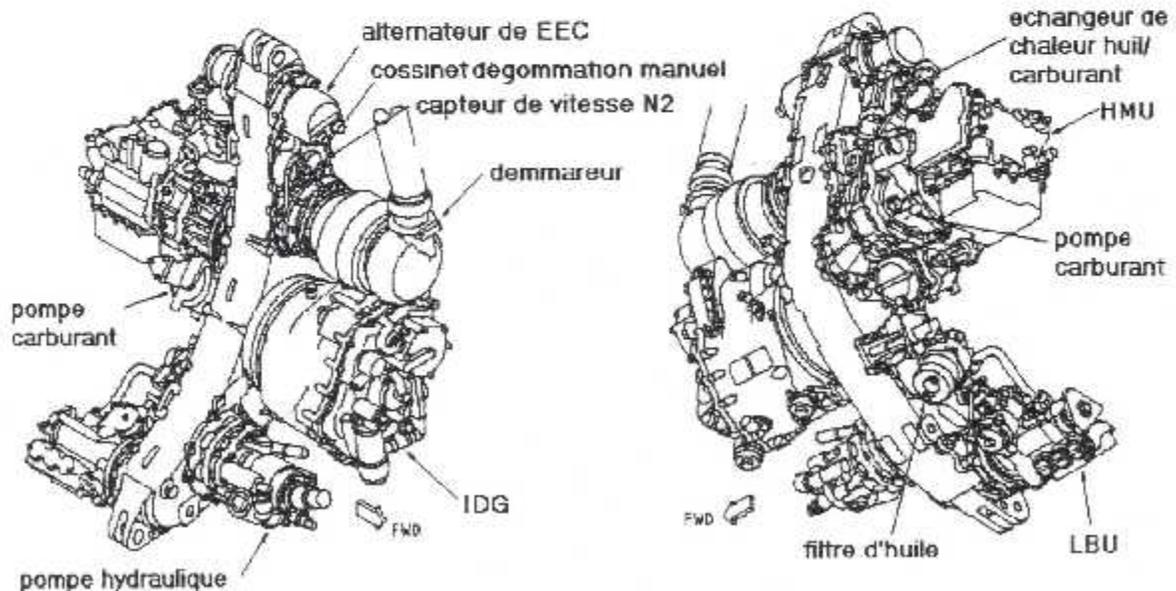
LES ACCESSOIRES DE LA GEARBOX (MODULE AGB)
